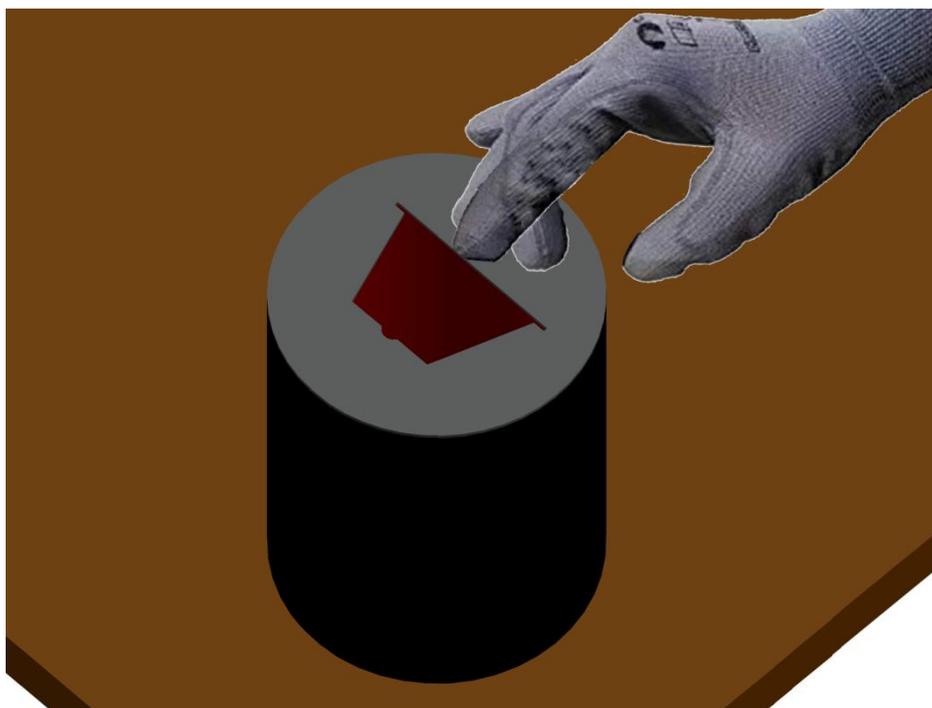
Sellado del conjunto con las piezas 1 y 3.
